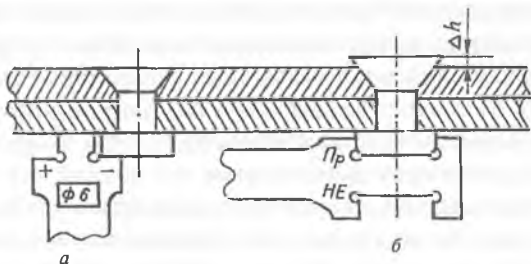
Контроль высоты — а и диаметра — б замыкающей головки заклепки шаблоном-калибром
